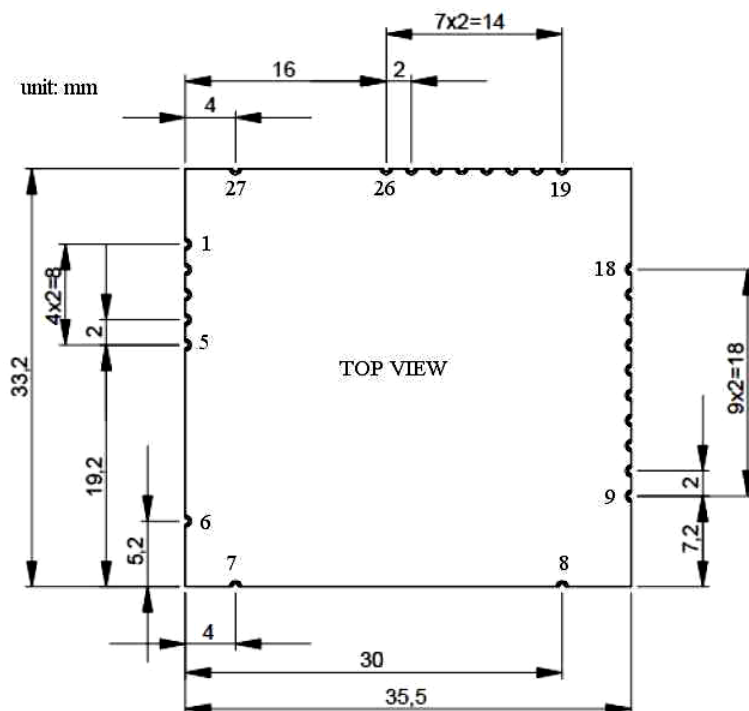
Габаритно-присоединительные размеры модуля GL8088s.
